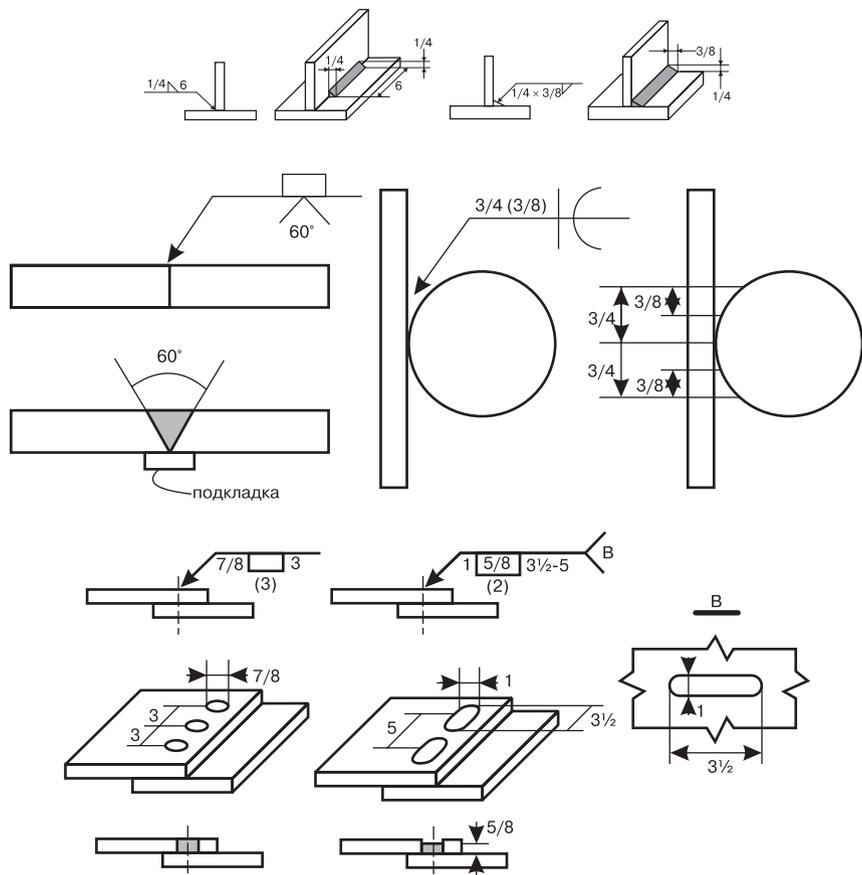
Примеры обозначения сварных соединений в соответствии с ANSI/AWS A2.4
